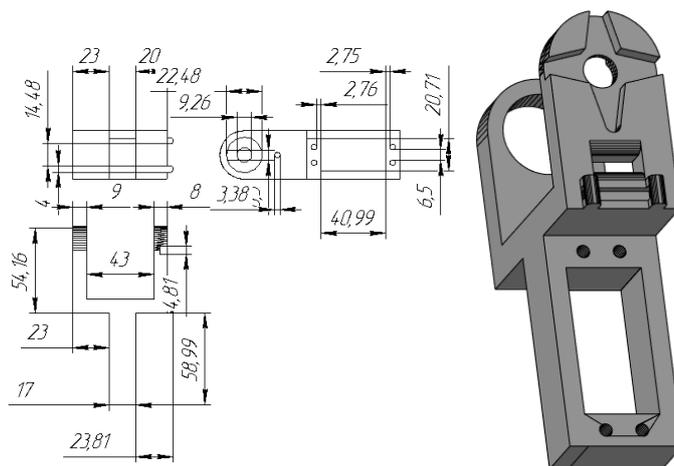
Модель и чертеж модуля конструкции корпуса
